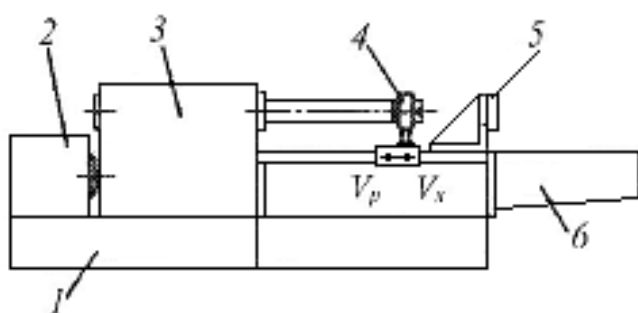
Загальний вигляд горизонтально-протяжного верстата
